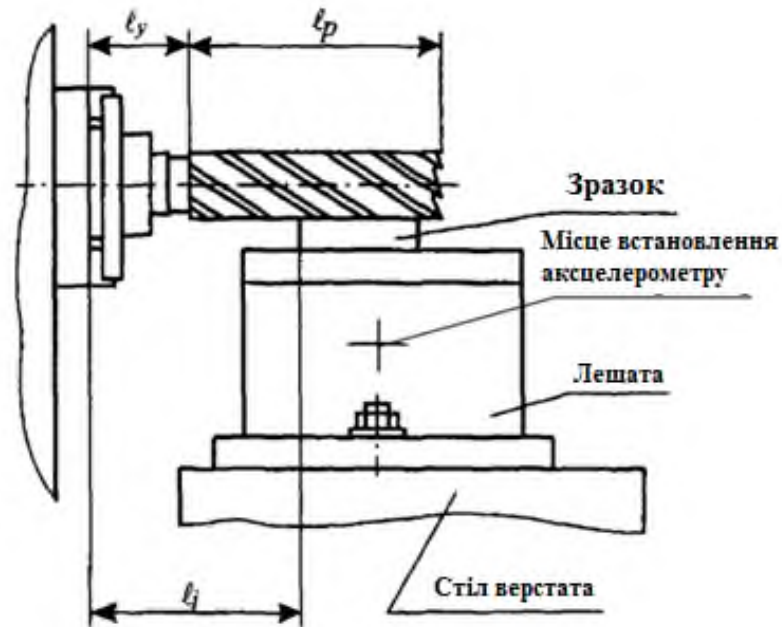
Схема установки кінцевої фрези відносно заготовки [9]
